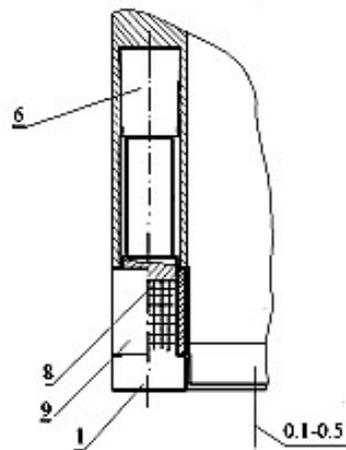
Резец с термомеханическим закреплением режущей пластины и хвостовика в корпусе инструмента
